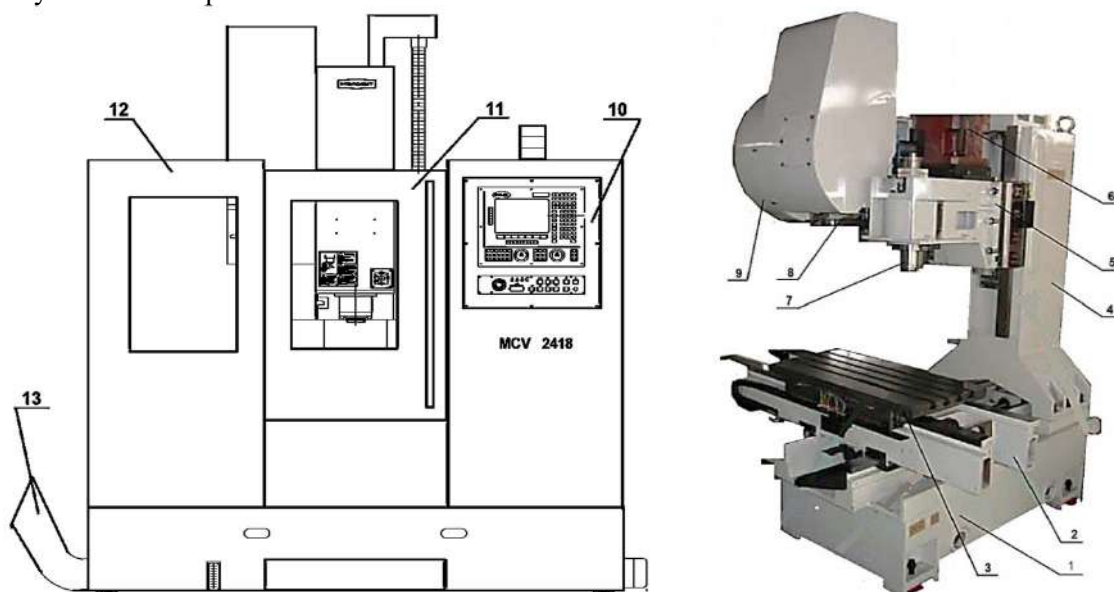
Вертикальний фрезерний верстат з ЧПК MCV 2418
